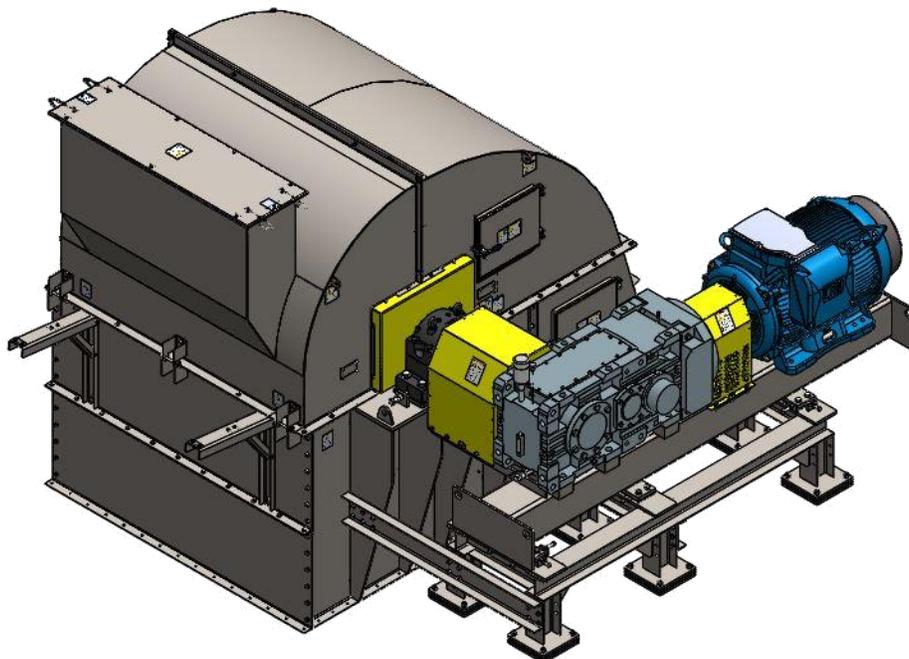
Acionamento interligado a Cabeça do Elevador
